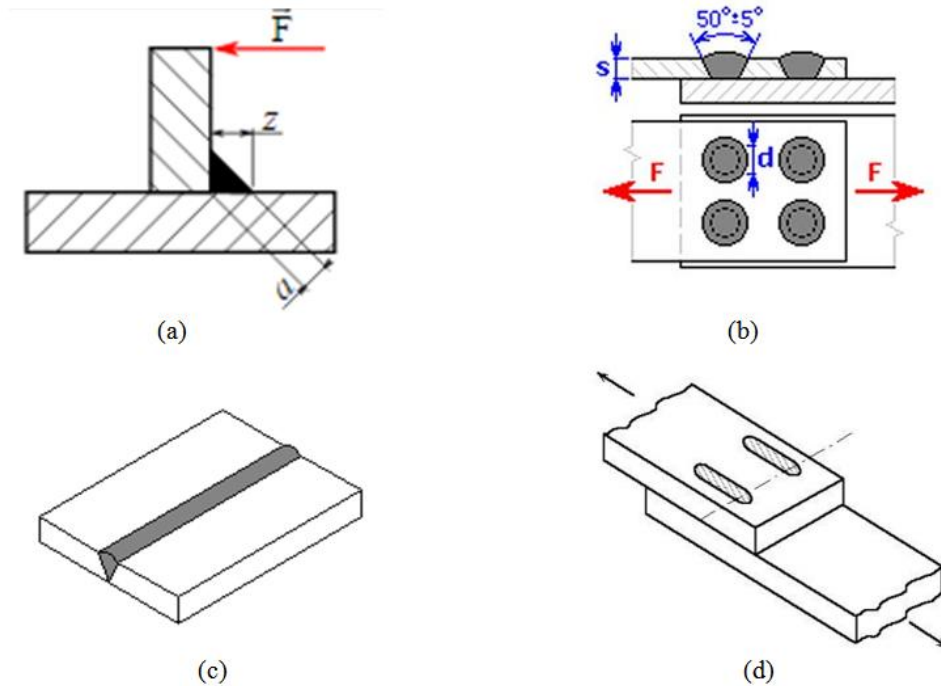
Quelques types de soudure appliquées en construction mécanique:
